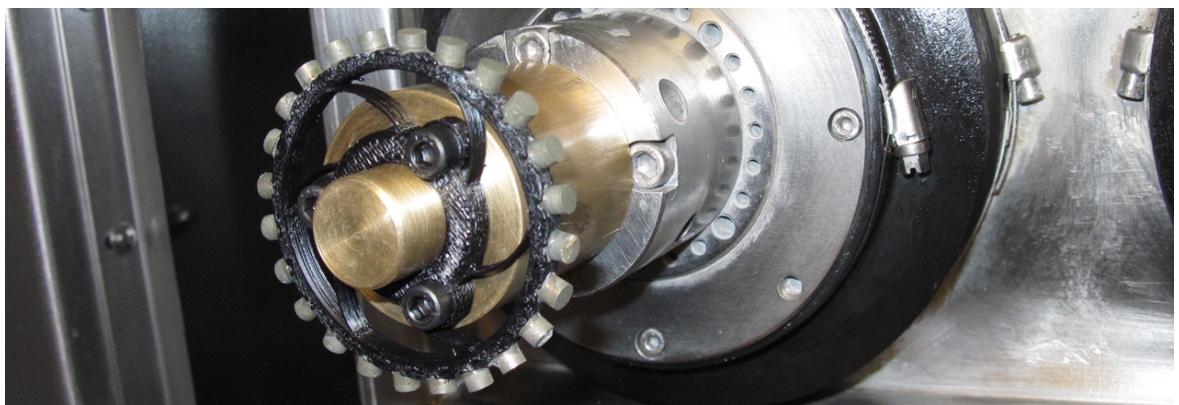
Bsp. Prototyp elastisches Schleifwerkzeug
